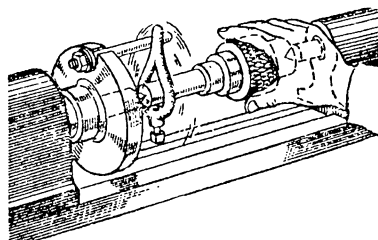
Притирка цилиндрических деталей на токарном станке
